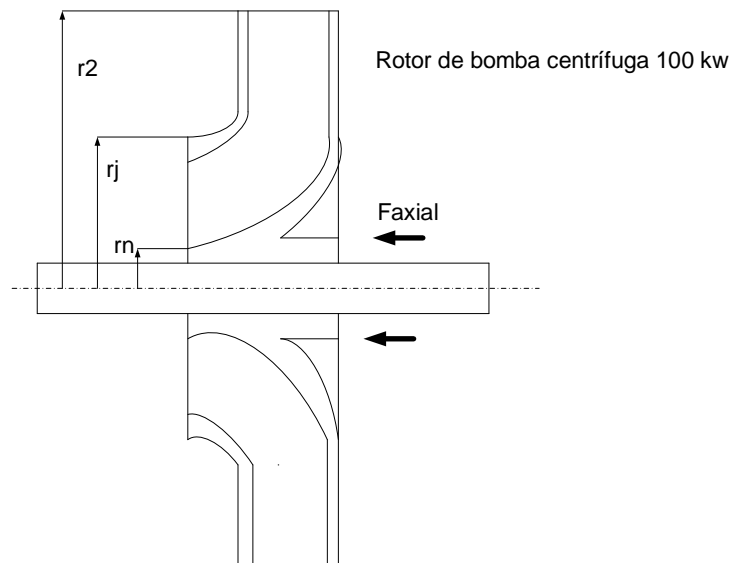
a: Radios de rotor de bomba centrífuga para cálculo de fuerza axial
